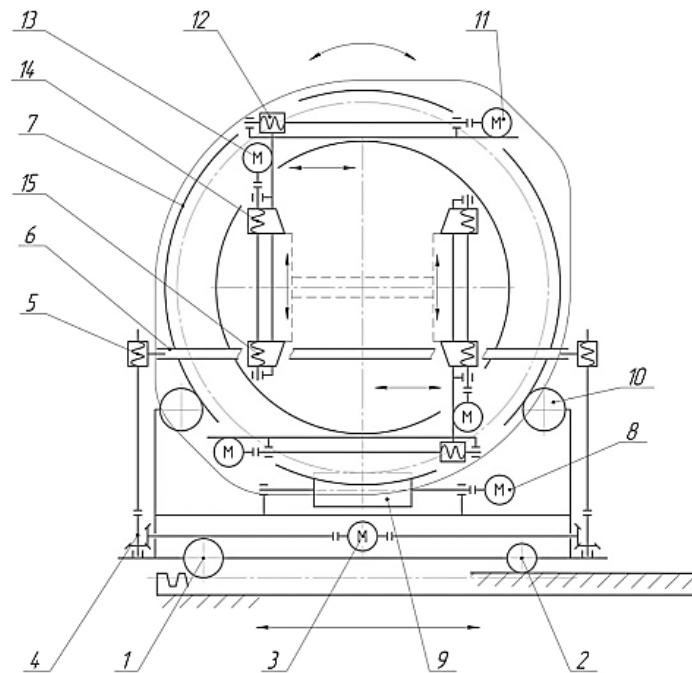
Схема поворотного портала-кантователя: 1 – передача «шестерня – рейка»; 2 – направляющая пара качения; 3 – электродвигатель; 4 – конический редуктор; 5 – винтовая пара; 6 – приемный ролик; 7 – опорно-поворотный круг; 8 – электродвигатель; 9 – червяк; 10 – пара качения; 11 – мотор-редуктор; 12 – винтовая пара; 13 – мотор-редуктор; 14 – винтовая пара; 15 – винтовая пара
